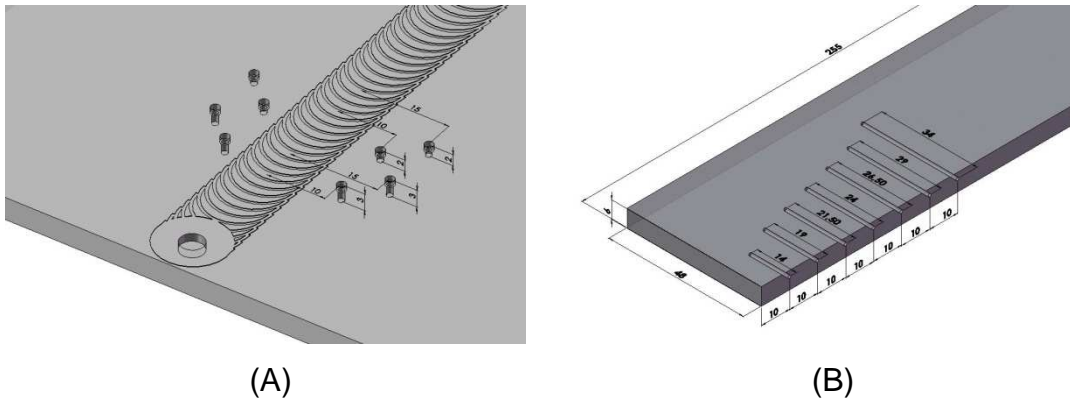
Representação esquemática do posicionamento dos termopares: (A) nas chapas soldadas por FSW e (B) nos *backing* de diferentes materiais (fonte: GKSS)
